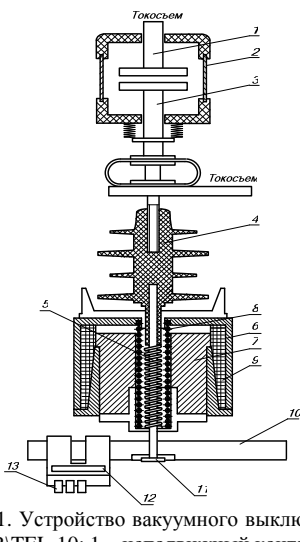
Устройство вакуумного выключателя ВВ\TEL-10: 1 – неподвижный контакт; 2, 4 – тяговые изоляторы; 3 – подвижный контакт; 5 – пружина поджатия; 6 – кольцевой магнит; 7 – якорь электромагнита; 8 – пружина отключения; 9 – катушка; 10 – вал; 11 – пластина; 12 – постоянный магнит; 13 – герконы
